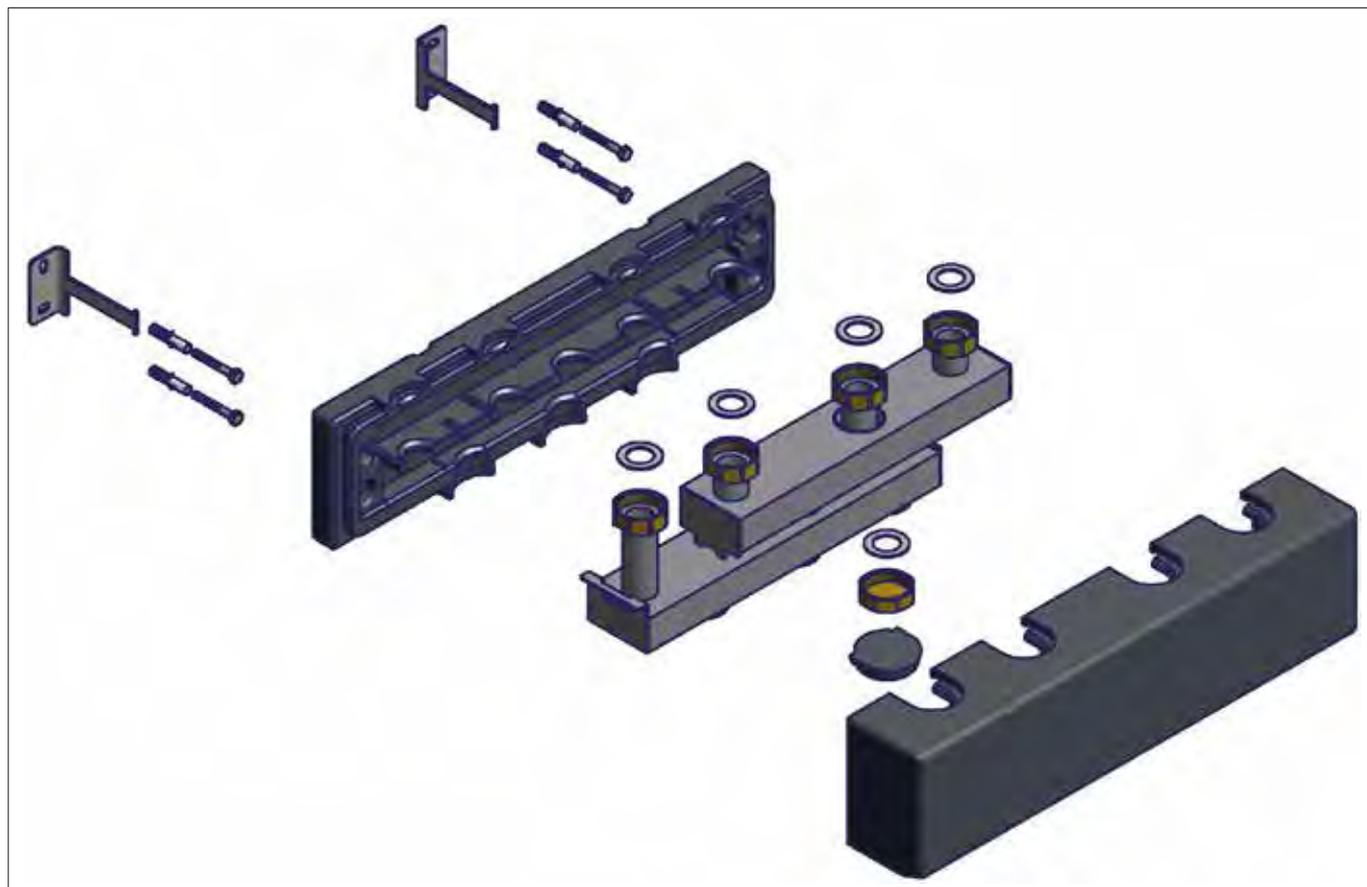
Настенный монтаж при помощи настенного кронштейна (опция) и крепежного набора
